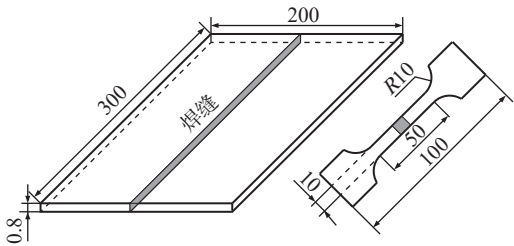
焊接试板及拉伸试件尺寸 (mm)
